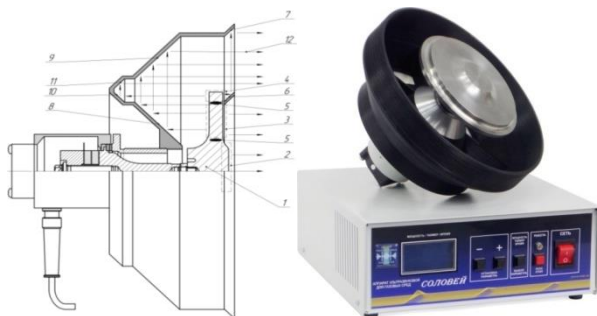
УЗ излучатель с фазовыравнивающими рупорами.
